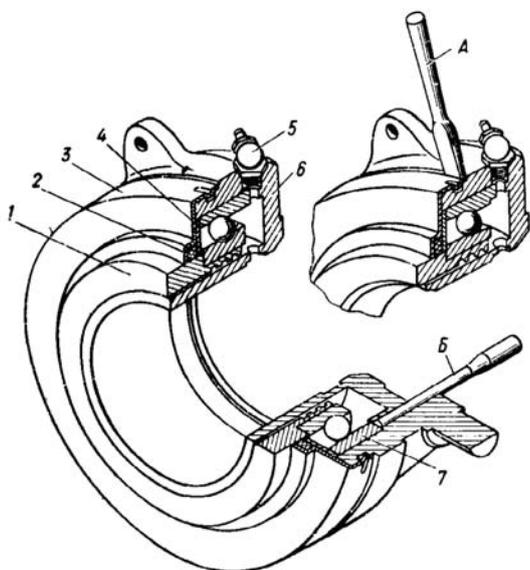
Разборка выжимного подшипника: 1 — упор выжимного подшипника; 2 — сальник; 3 — крышка; 4 — шайба; 5 — масленка; 6 — корпус; 7 — подшипник; А — лопатка монтажная; Б — наставка
